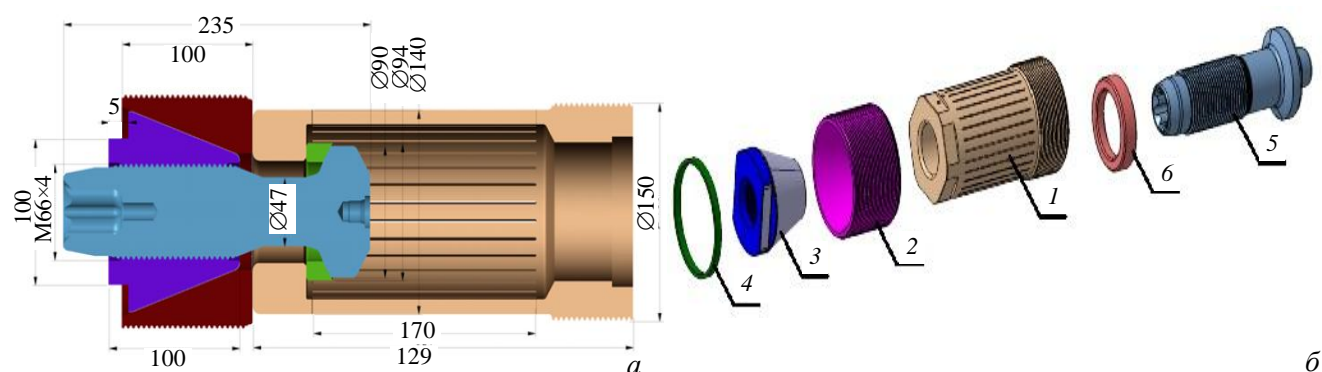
Общий вид ГМО в сборе (а) и схема ГМО (б): 1 — гибкий картридж; 2 — коническая втулка; 3 — коническая гайка; 4 — проставка; 5 — болт М64; 6 — сферическая шайба
